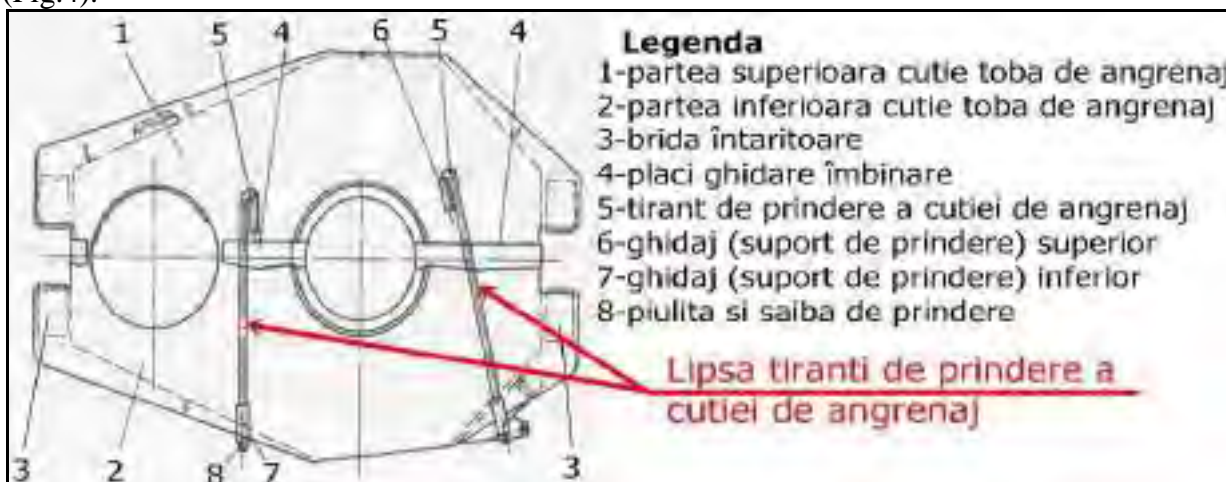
Ansamblu carcasă cutie tobă de angrenaj
